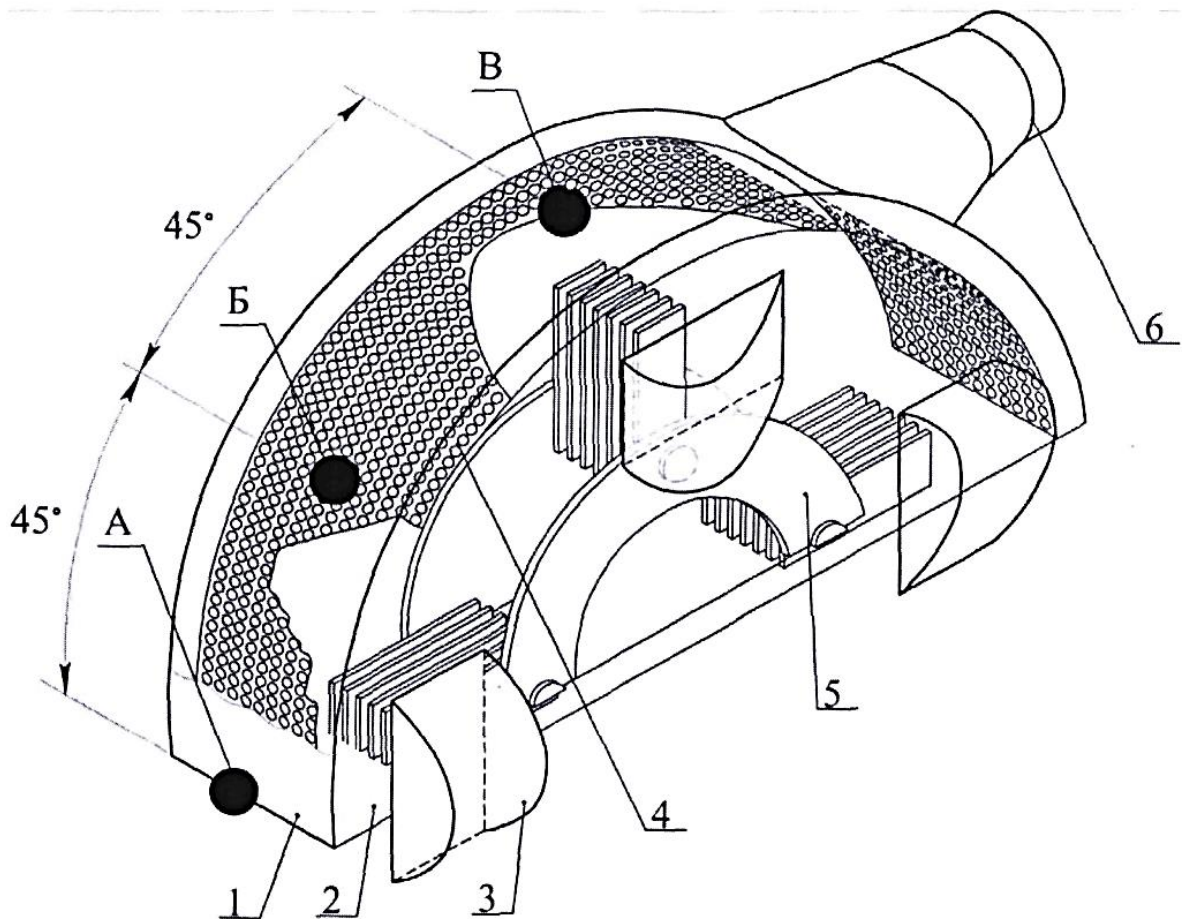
Фрагмент дробарки: А, Б, В - точки вимірювання тиску дробильної камери; 1-корпус дробарки; 2-кришка дробильної камери; 3-вихрова камера; 4- решето; 5 молотковий ротор; 6- завантажувальний патрубок
